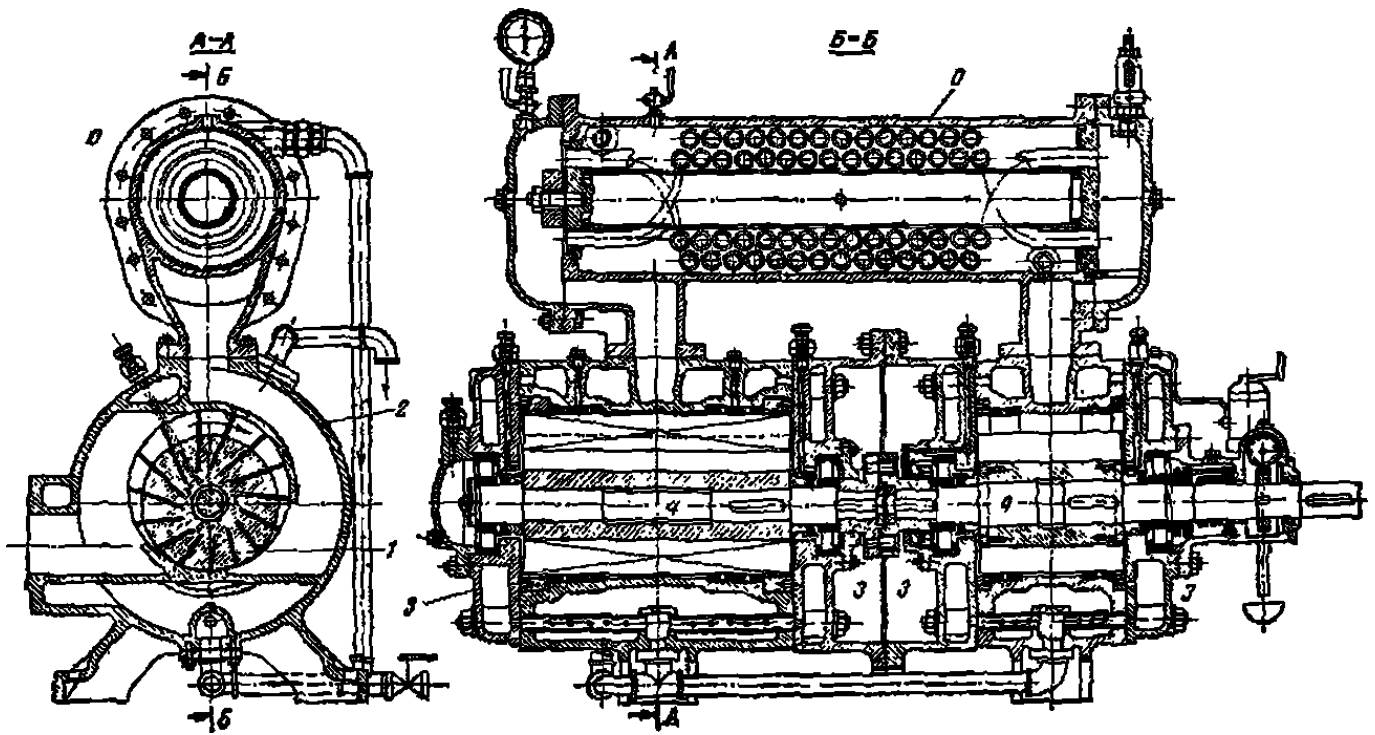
Гвинтовий компресор із двома черв'яками
